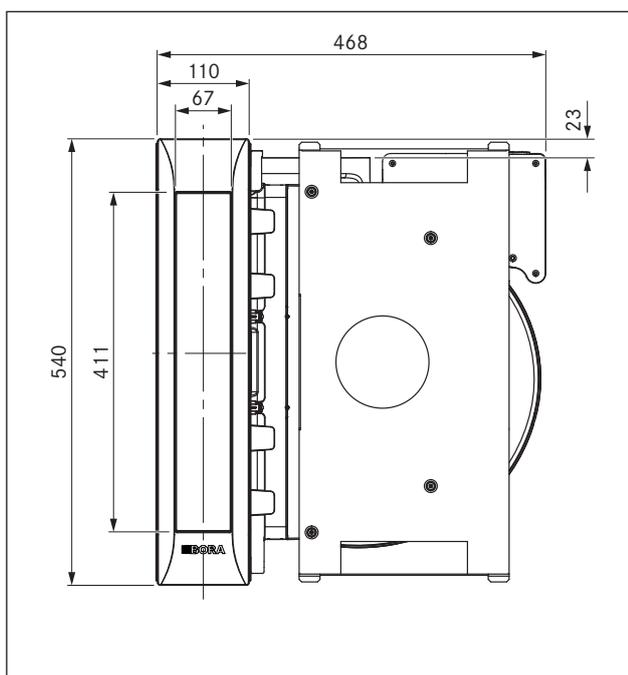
Dimensions PKAS, PKASAB vue du dessus
